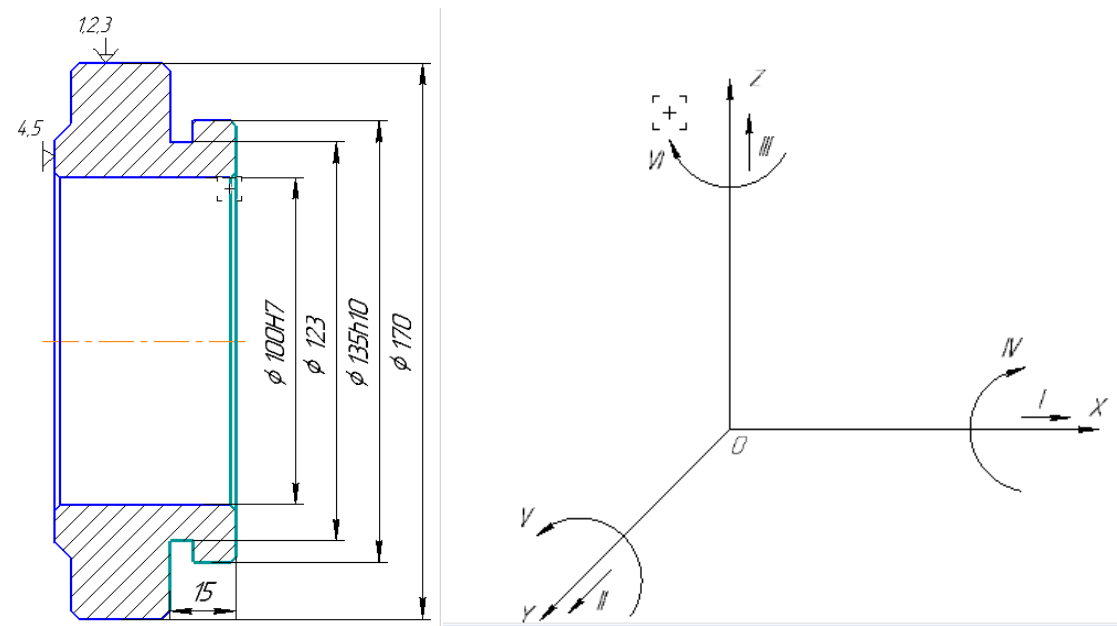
Схема базування заготовки в трикулачковому патроні
